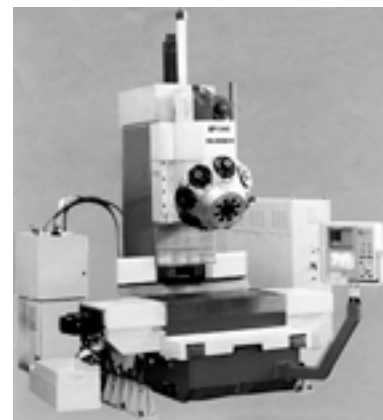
Вертикально-фрезерный станок MA-655 A14 с ЧПУ и автоматической сменой инструмента
